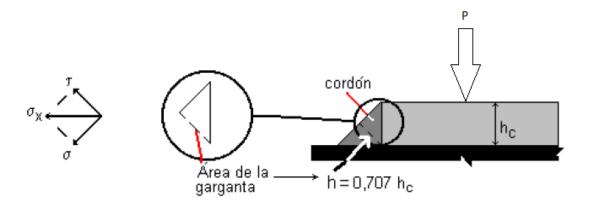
Nomenclatura para cordón de soldadura
